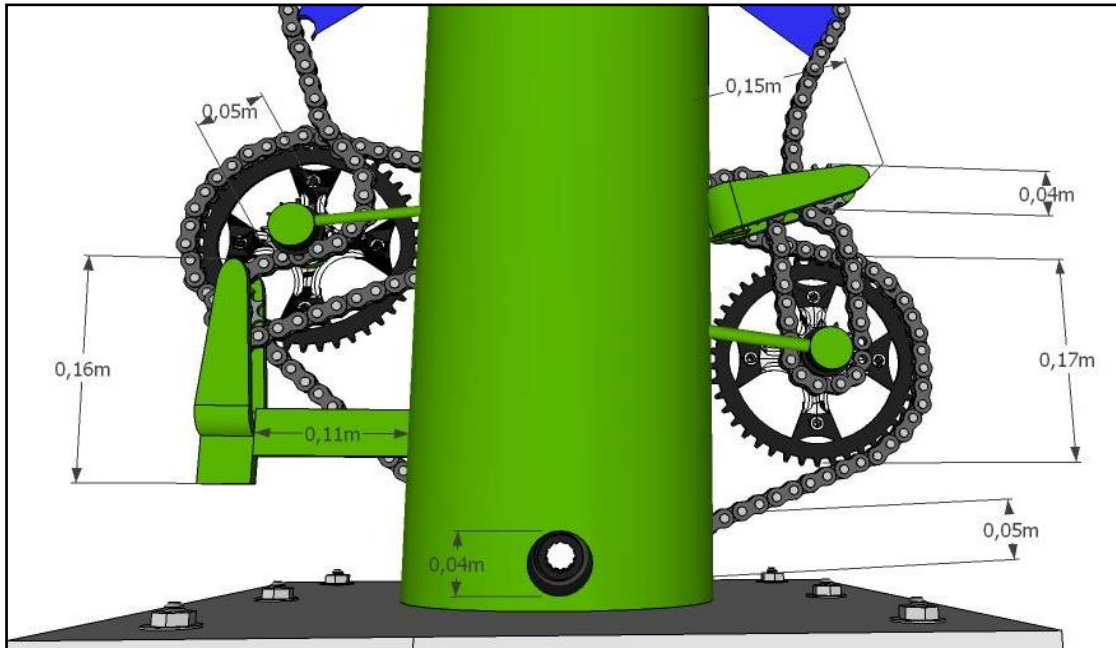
Detalle de la geometría del sistema de engranajes del subibaja a utilizar como módulo de tracción.
